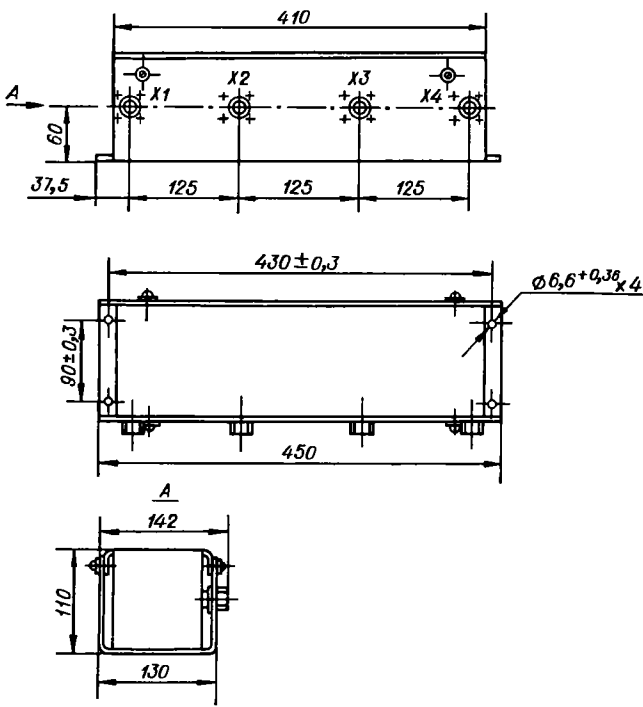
Габаритные и установочные размеры блока трансформаторов БТ12:
